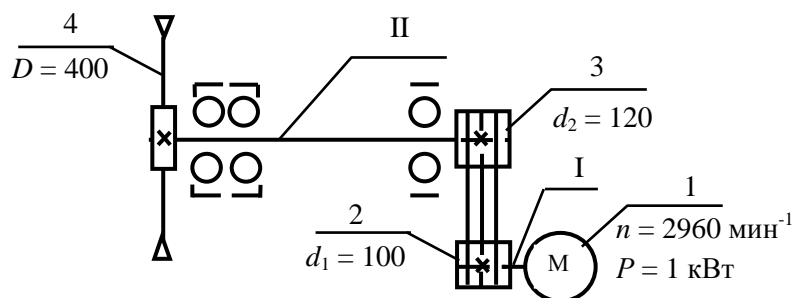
Кинематическая схема механизма главного движения круглопильного станка
